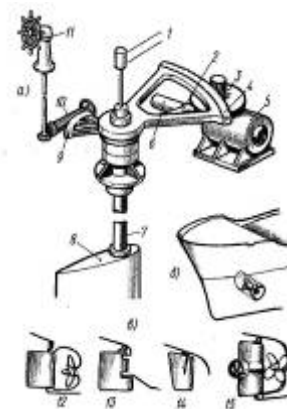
Элементы рулевого устройства (а), подруливающее устройство (б) и типы рулей (в). 1 — к рулевой рубке; 2 — румпель; 3 — редуктор; 4 — рулевой сектор; 5 — двигатель; 6 — пружина; 7 — баллер руля; 8 — перо руля; 9 — сектор аварийного привода; 10—„червяк“; 11—штурвал; 12 — обыкновенный руль; 13 — полубалансирный руль; 14 — балансирный руль; 15 — активный руль
